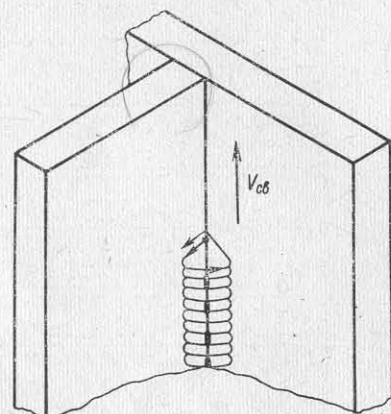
Схема колебательных движений при сварке тавровых соединений калибром более 6 мм.
